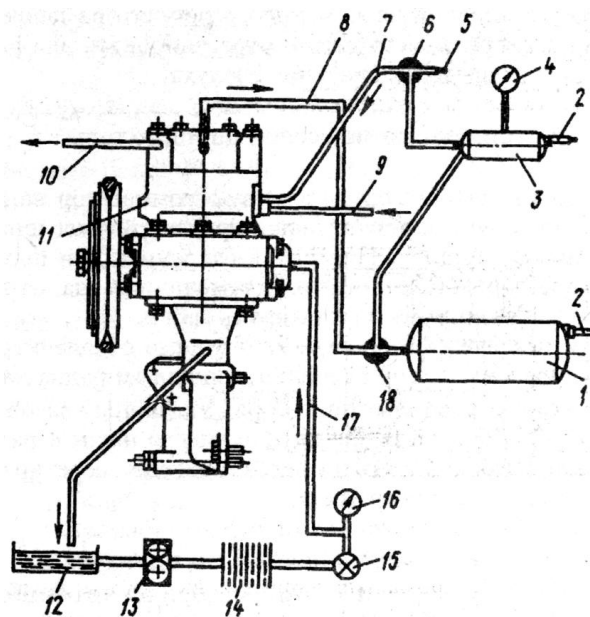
Схема стенда 70-7020-1502 для испытания компрессоров:
